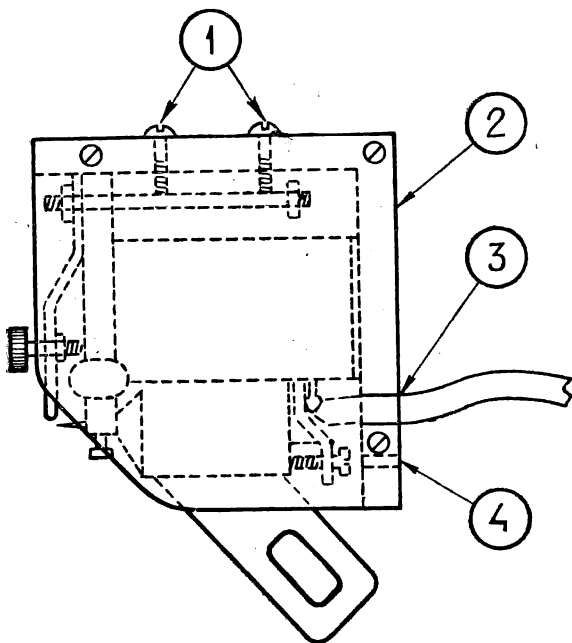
1—винты крепления свинцовой крышки, служащей добавочным грузом. 2—свинцовая крышка. 3—выводной шнур. 4—отверстие для отвертки для натяжки струны крепления якоря
